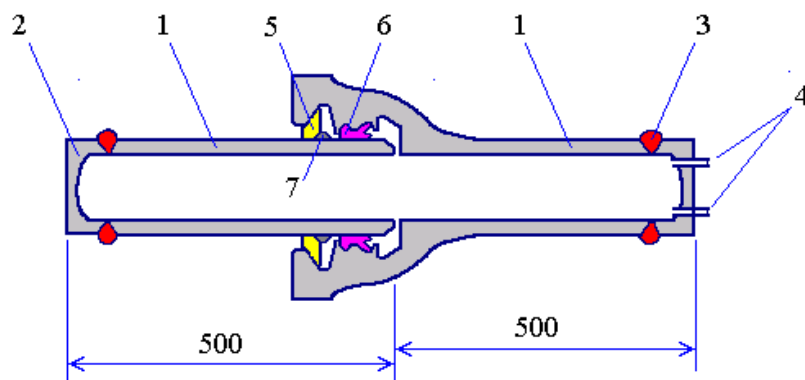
Образец для гидроиспытаний соединения “RJ” (1 – катушки трубы из ВЧШГ; 2 – приварные заглушки; 3 – сварной шов; 4 – штуцера для закачки испытательной жидкости и выпуска воздуха; 5 – стопор; 6 – уплот. резиновое кольцо; 7 – наплавленный валик)
